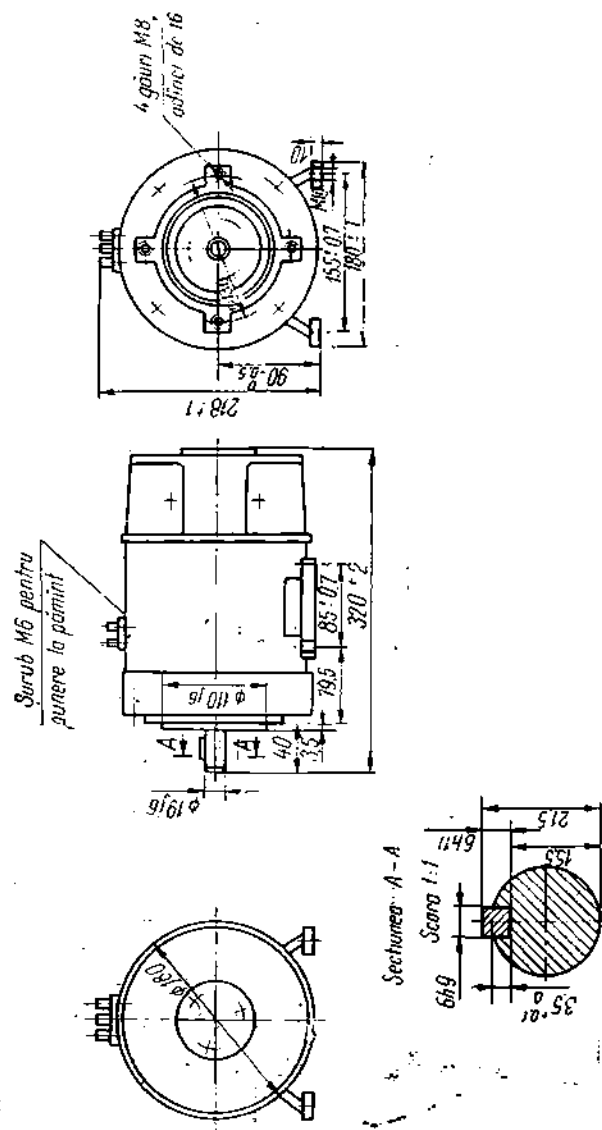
Motor tip Ce 90 F — 0,250 kW. Dimensiuni de montaj.
